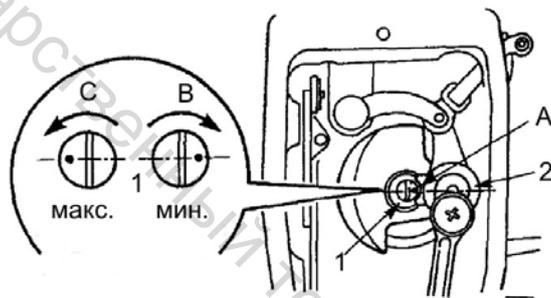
Регулировка смазки иглы и нитепритягивателя
